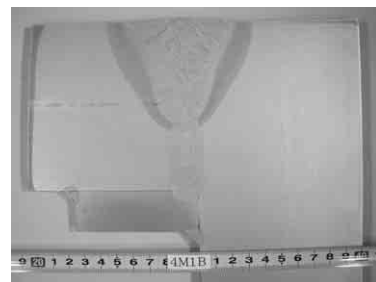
ボックス柱角継手溶接部のマクロ写真
